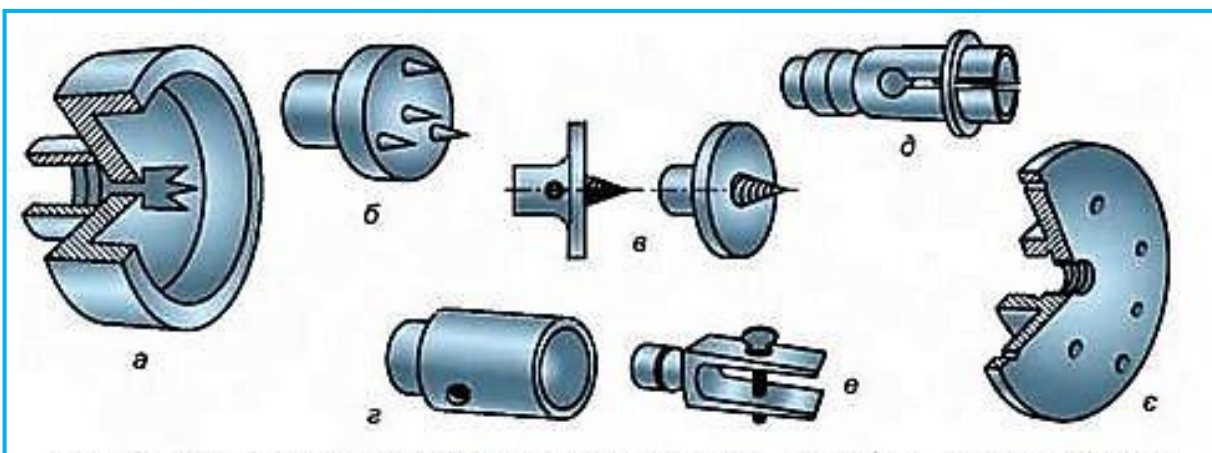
Технологічні пристрої токарного верстата: а – тризуб; б – патрон із шипами; в – патрон з конічним гвинтом; г – чашковий патрон; д – цанговий патрон; е – лещатний патрон; є - планшайба
